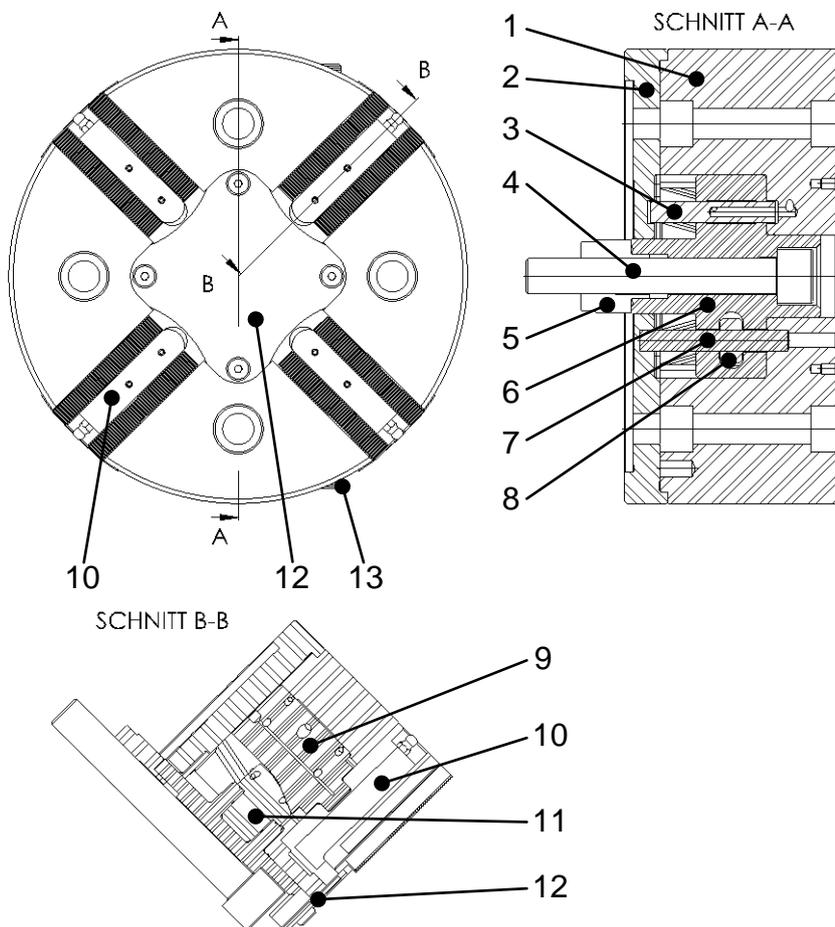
Struttura del mandrino di serraggio InoFlex®
